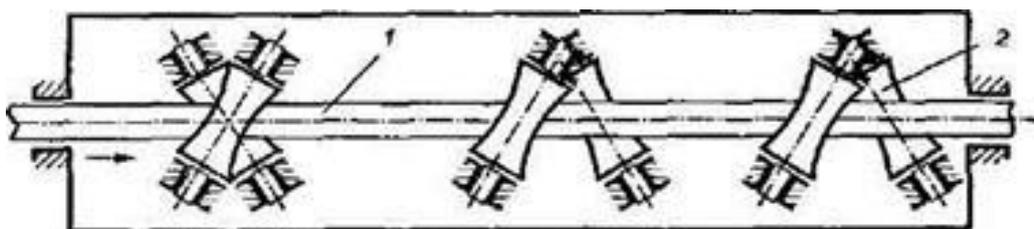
Схема правильно-рихтовочного устройства станка
